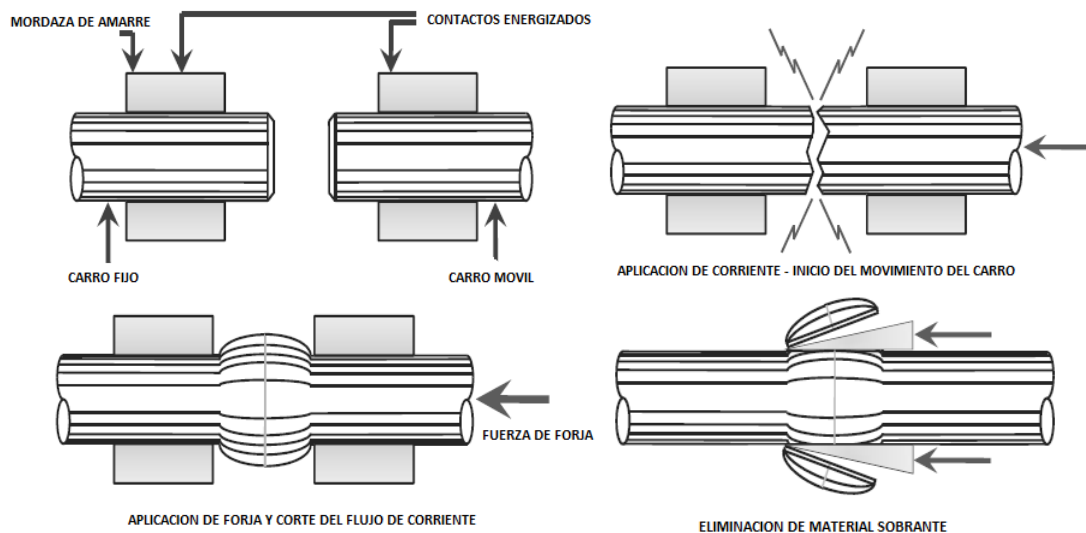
Esquemático del proceso de soldadura a tope por destello. (Kim, So, & Kang, 2009)
